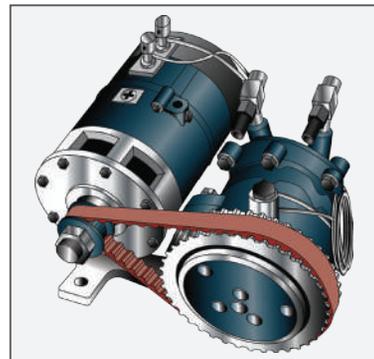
B - Compressor acionado por intermédio de motor elétrico
